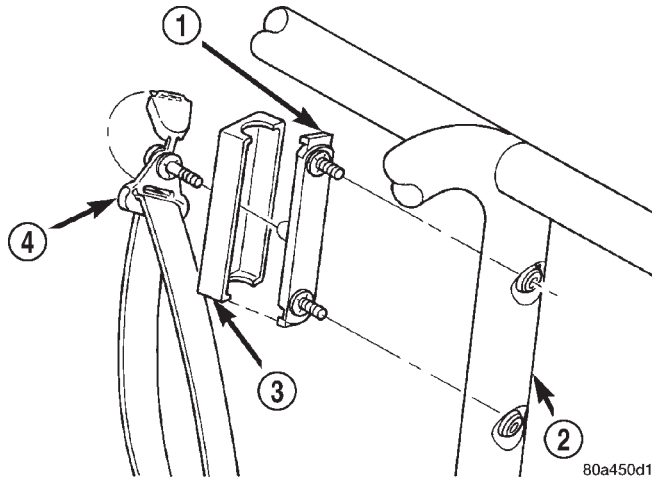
Dispositivo de doblez de cinturón de hombro delantero
